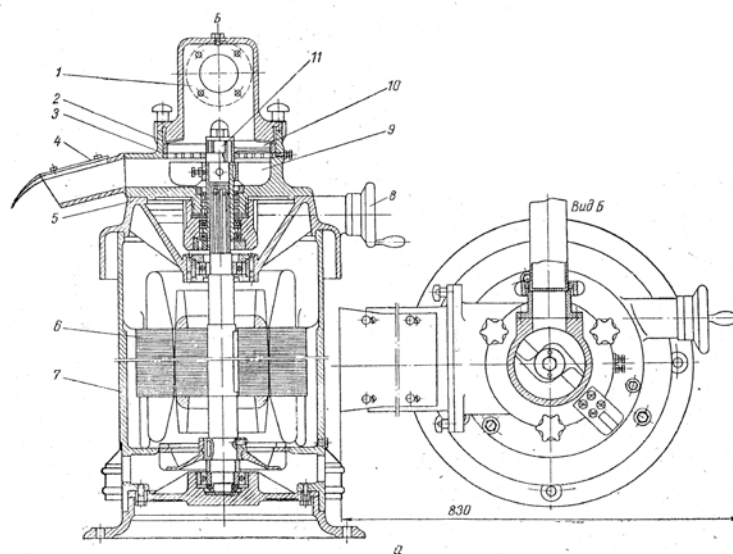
Емульситатор АТИМ-1: 1 – завантажувальна головка; 2 – опірне кільце; 3 – нерухома ґратка; 4 – вивантажувальний лоток; 5 – головка станини; 6 – електродвигун; 7 – вертикальний корпус; 8 – регулятор зазору; 9 – лопатка для вивантаження; 10 – рухомий ніж; 11 – вал
